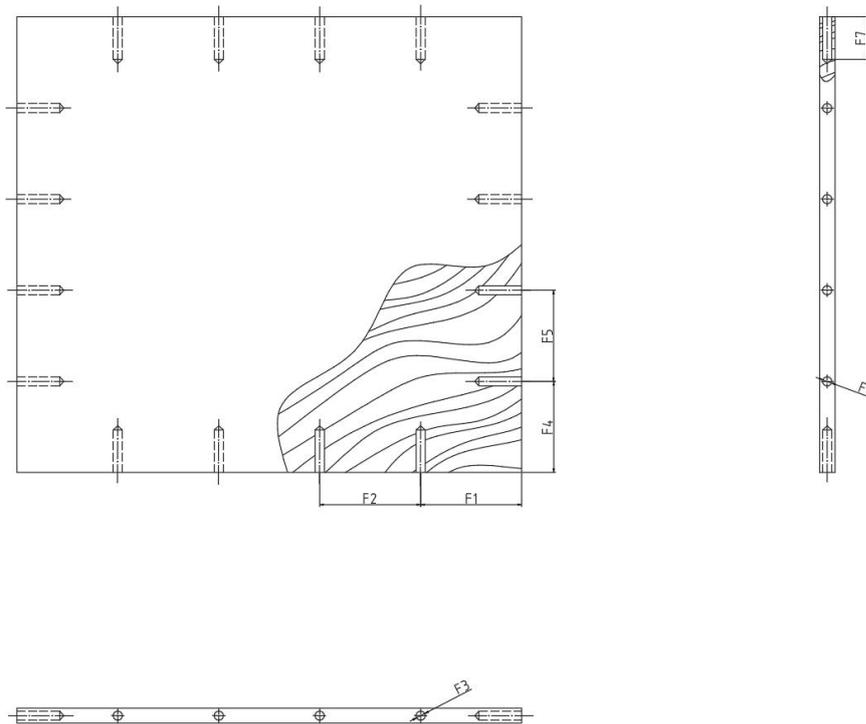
Plano Dimensionado Previo de la Trasera Cajón 2.1.2
